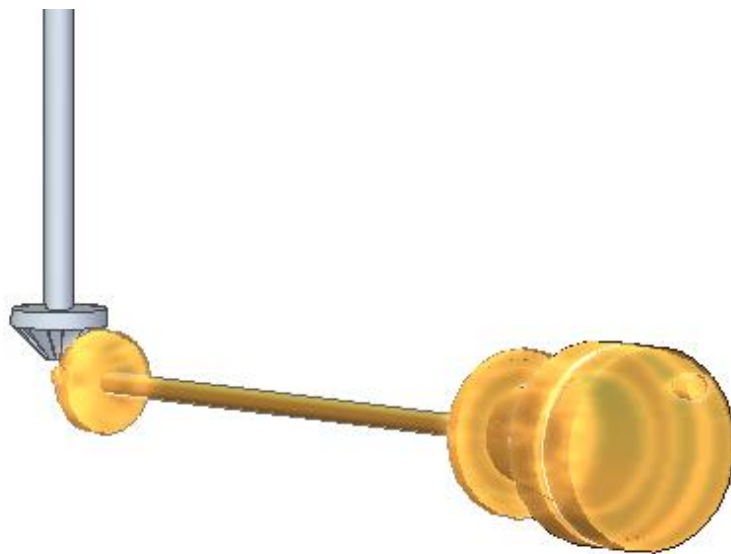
Eje horizontal con engranaje cónico
